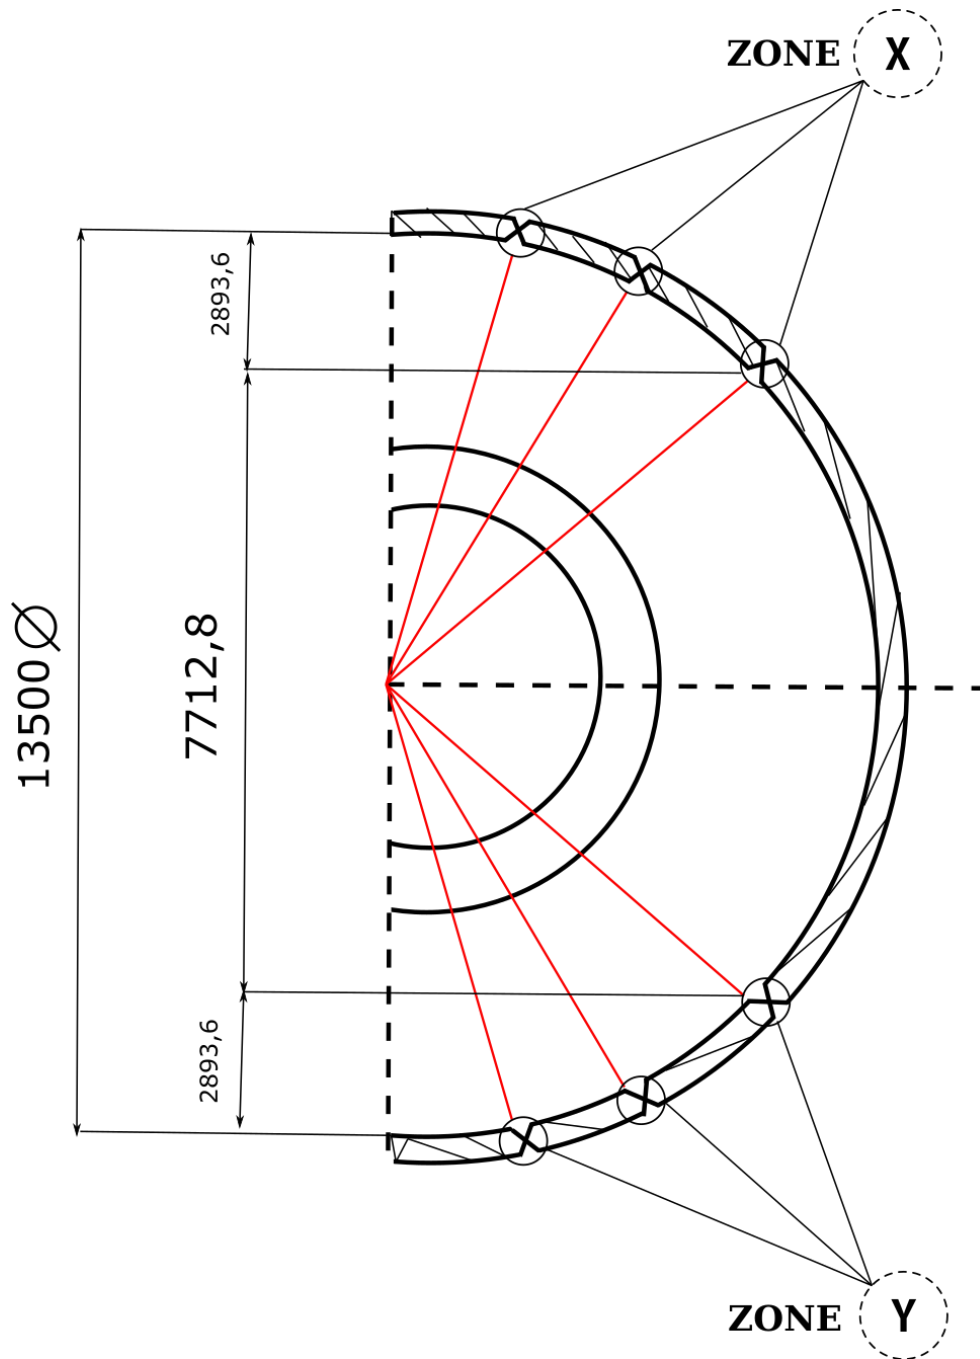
disposition des joints de la soudure pour la sphère
